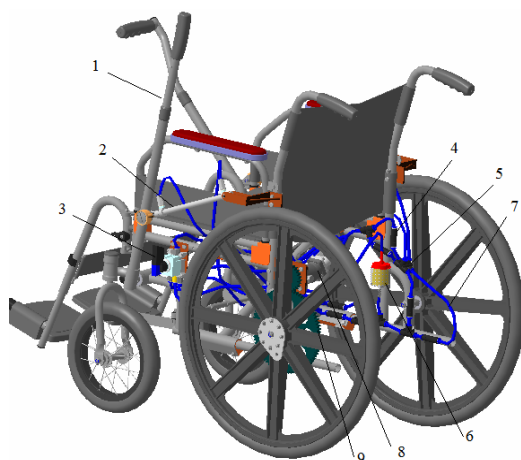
Компоновочная схема инвалидного кресла-коляски: 1 – рычаг управления; 2 – тройник; 3 – гидроцилиндр; 4 – гидрораспределитель; 5 – гидробак с фильтроэлементом; 6 – гидромотор; 7 – подшипник; 8 – гидромотор; 9 – редуктор
